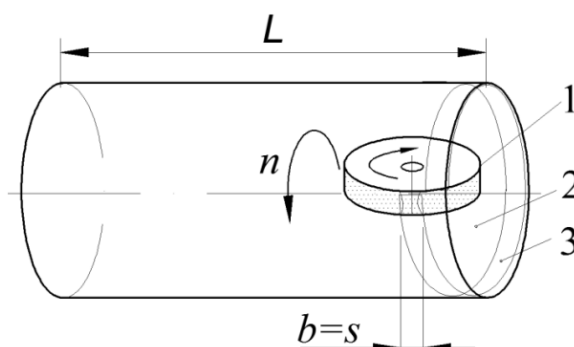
Схема обработки отверстия цилиндра абразивным инструментом: 1 – войлочный круг с наклеенным абразивным порошком; 2 – обрабатываемый цилиндр; 3 – шлифованная полоса;  $b$  – ширина пятна контакта;  $S$  – подача;  $n$  – частота вращения детали;  $L$  – длина детали
